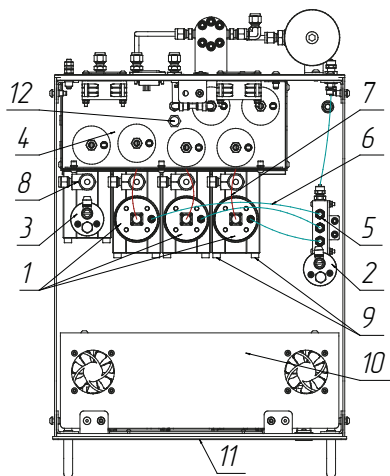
Вид сверху на калибраторы со снятыми крышками
